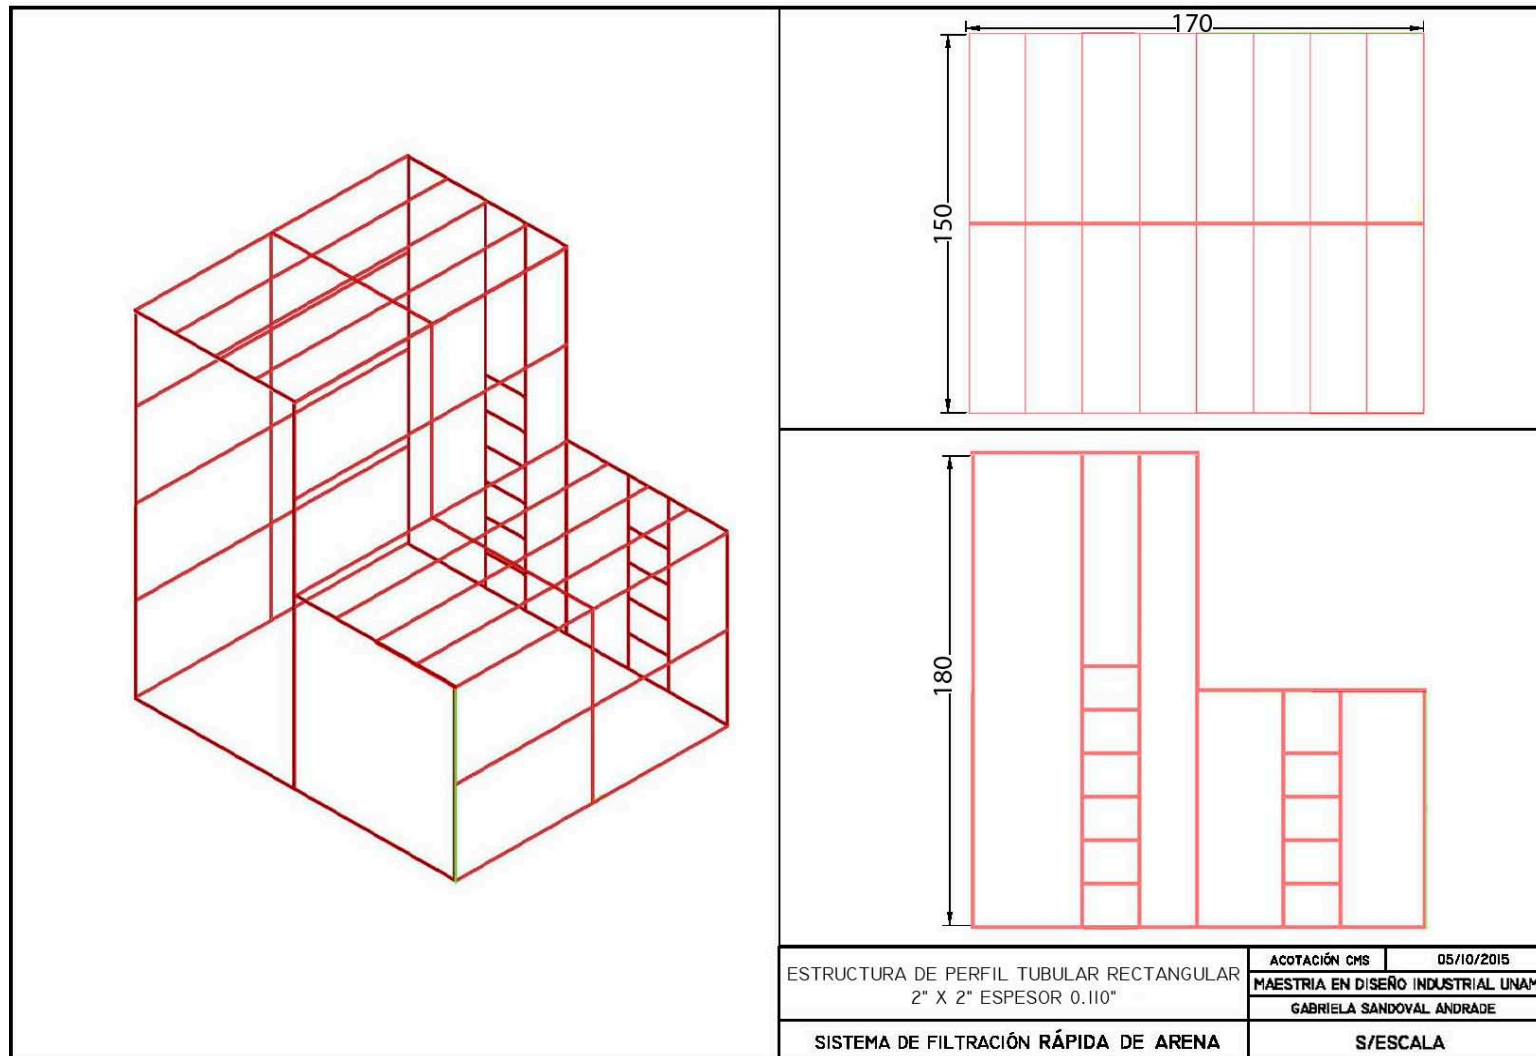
Detalle y diseño de estructura de PTR. Fuente: elaboración propia.
